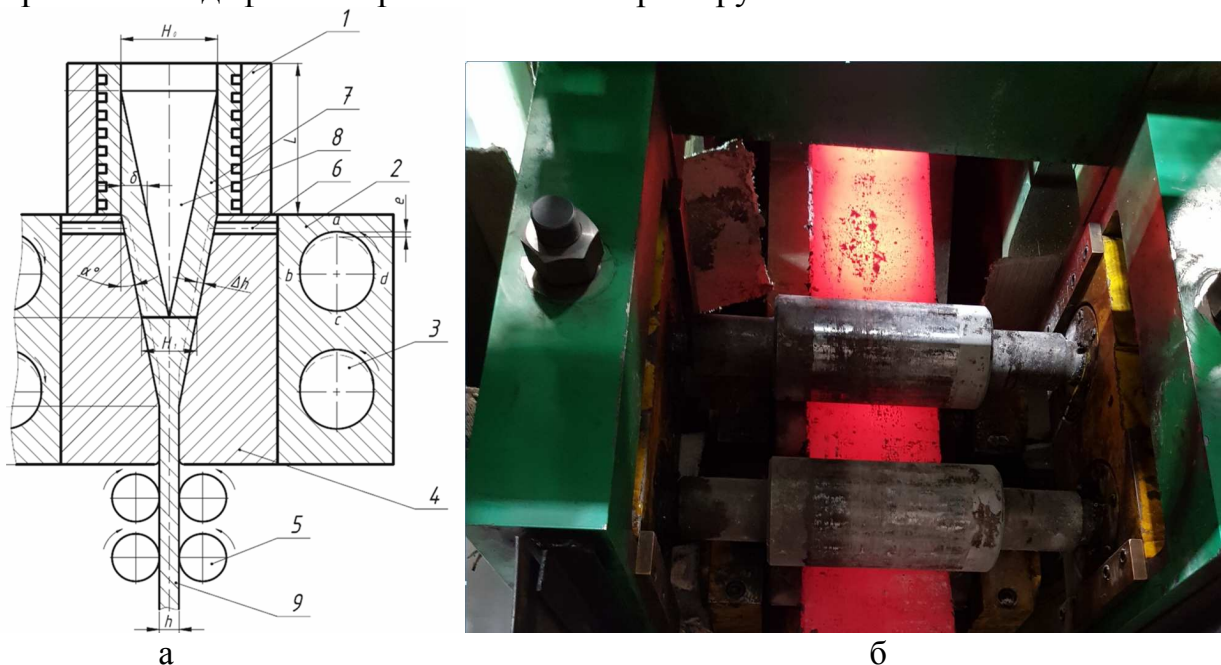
Схема получения полосы на установке (а) и вид полосы вытягиваемой роликами тянущего устройства (б): 1 – кристаллизатор; 2 – суппорт; 3 – валы эксцентриковые; 4 – бойки; 5 – ролики тянущего механизма; 6 – каналы подачи смазки; 7 – затвердевшая оболочка; 8 – жидкая фаза; 9 – полоса
